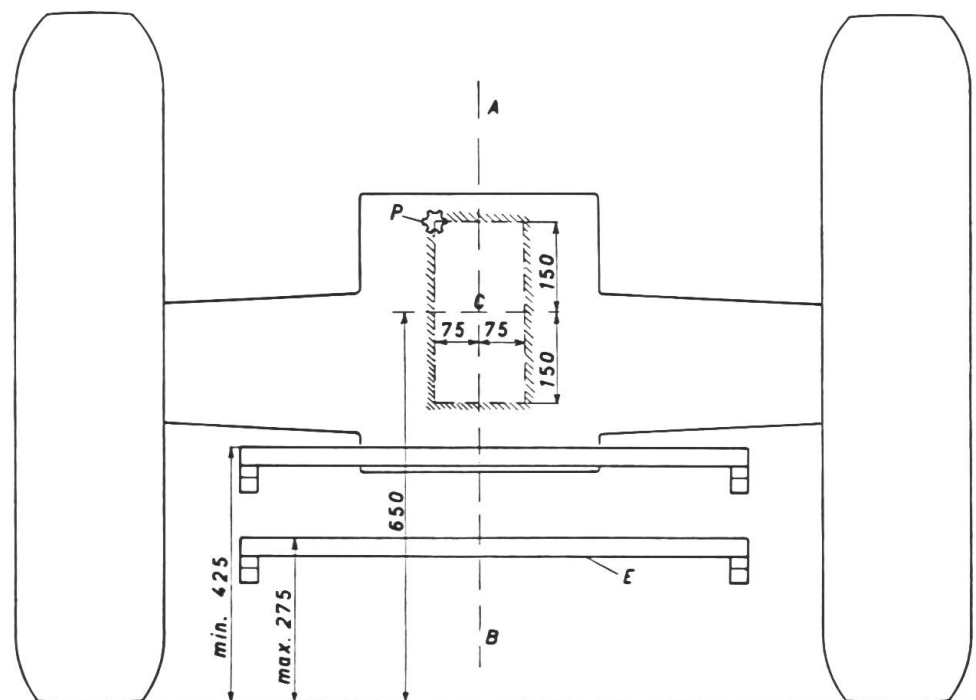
Emplacement de la prise de force par rapport au plan d'appui et au plan de symétrie du tracteur (cotes en mm).
